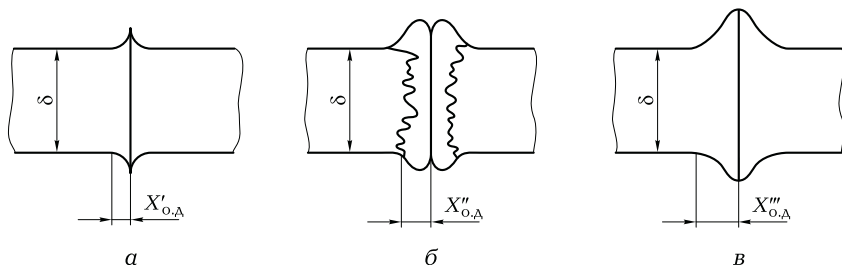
Формы стыковых соединений в результате ударно-стыковой сварки [а], стыковой сварки оплавлением [б] и стыковой сварки сопротивлением [в]:
